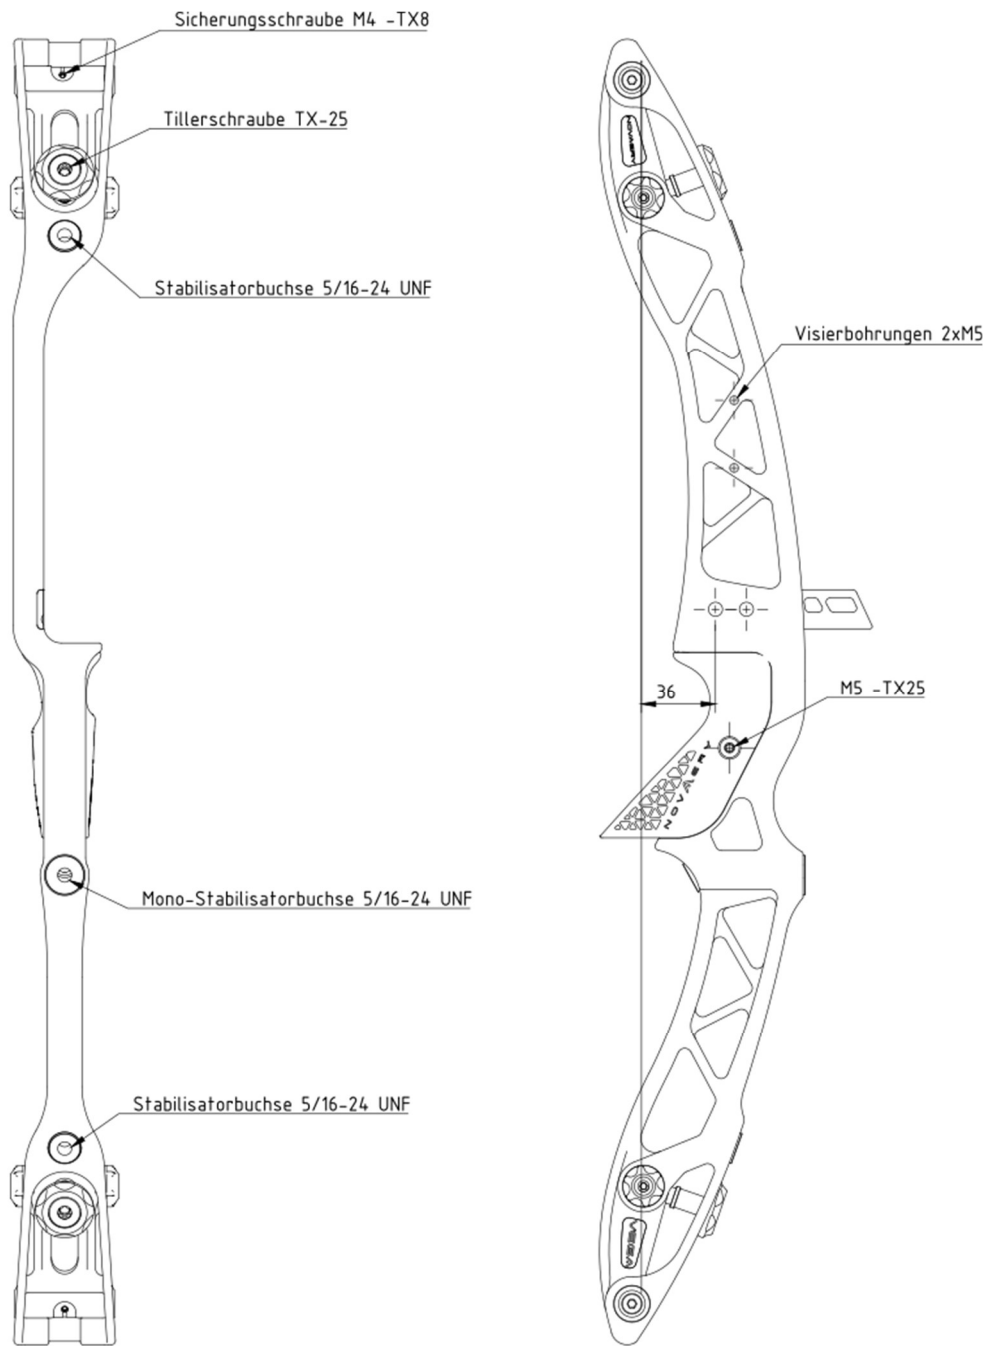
Basisgeometrie, Gewinde und TORX-Schlüssel-Größen
